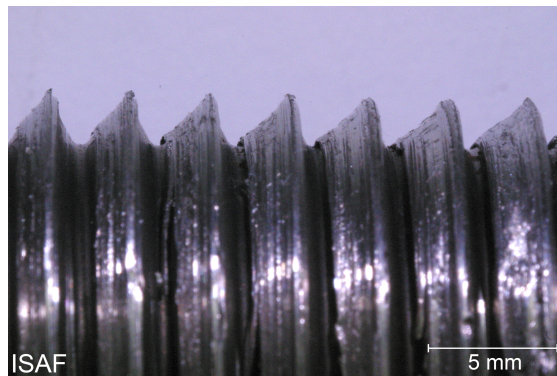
Gewindeprüfkörper axial belastet mit 120kN (Bolzen)
